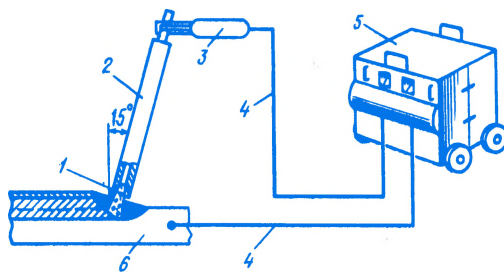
Сварочная электрическая цепь с дугой
